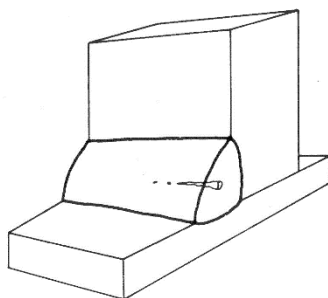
Representação esquemática de uma inclusão sólida num cordão de soldadura [5].
